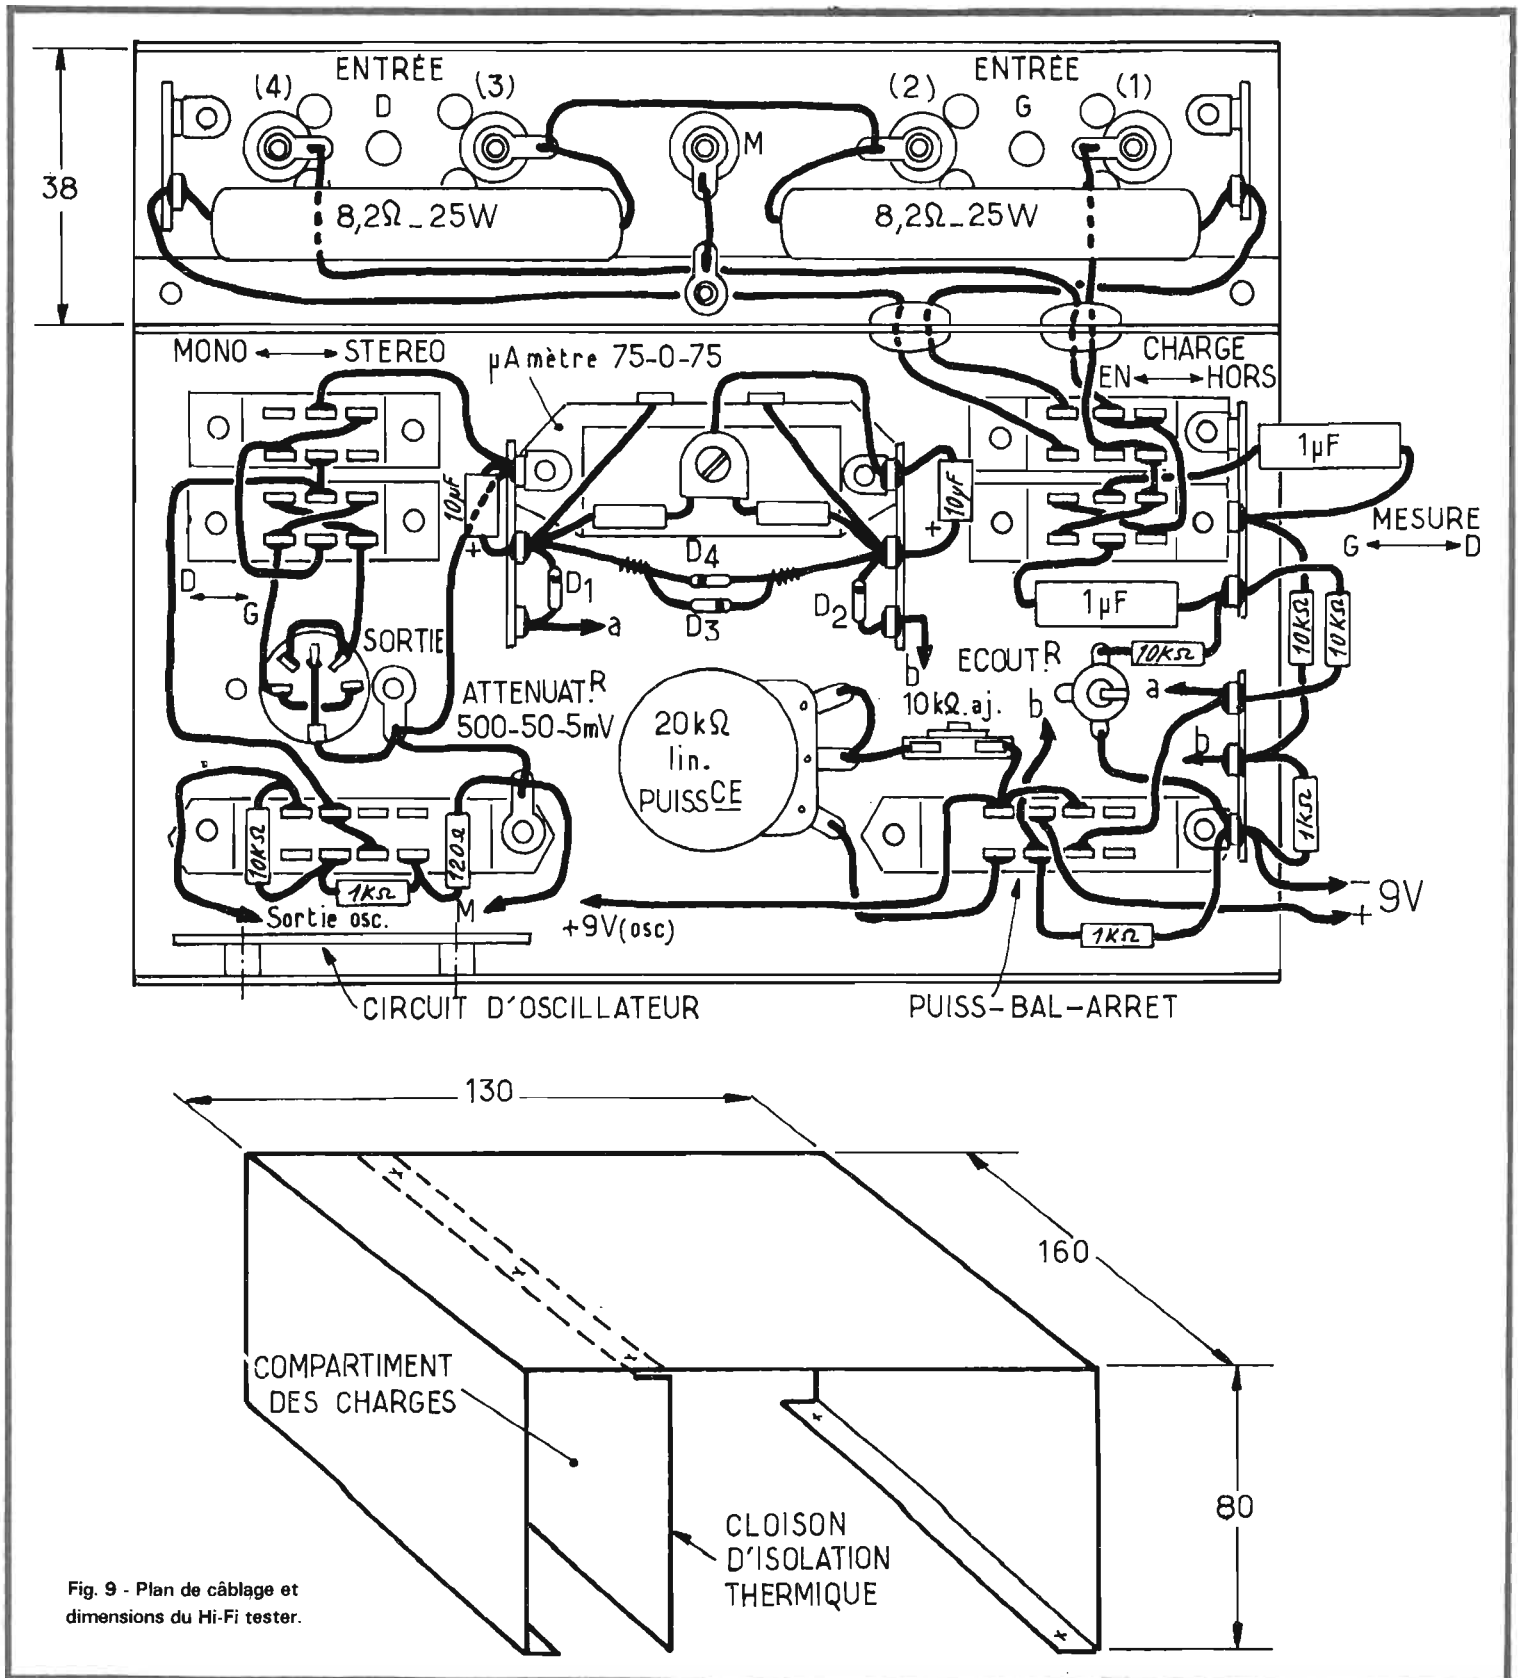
Plan de câblage et dimensions du Hi-Fi tester.
